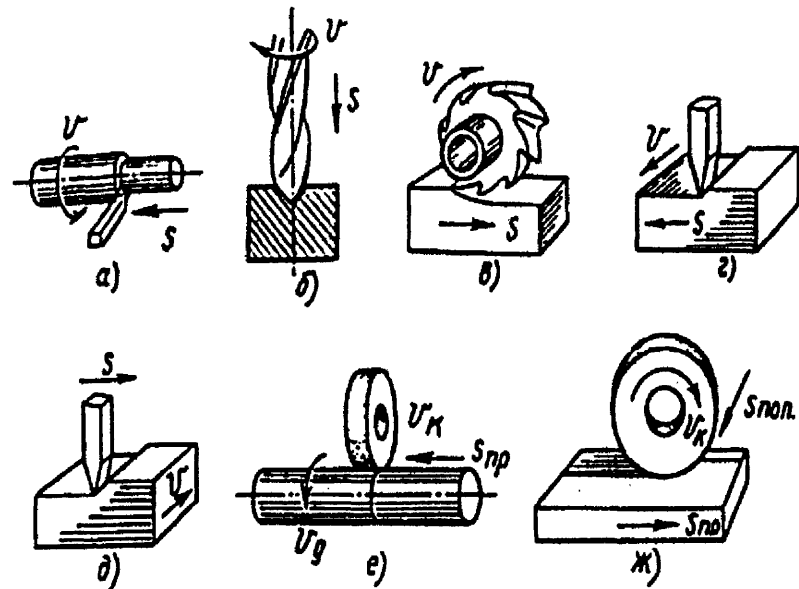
Виды обработки металлов резанием: а – точение; б – сверление; в – фрезерование; г, д – строгание; е, ж – шлифование
